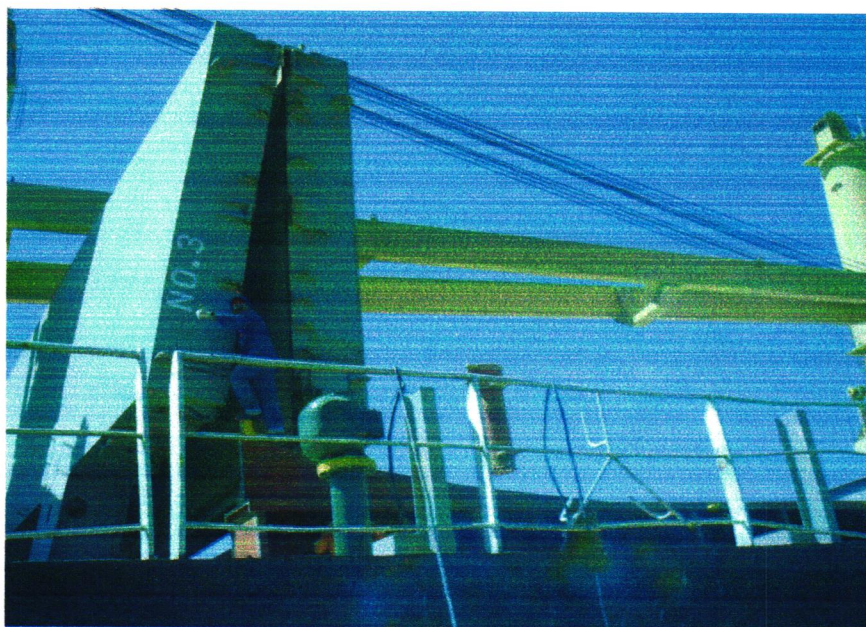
Caldeiraria e soldagem nos porões de navios.
